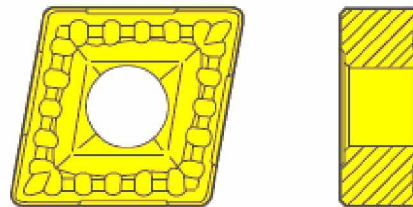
Ромбічна пластина для чорнової обробки CNMG120404-R4
